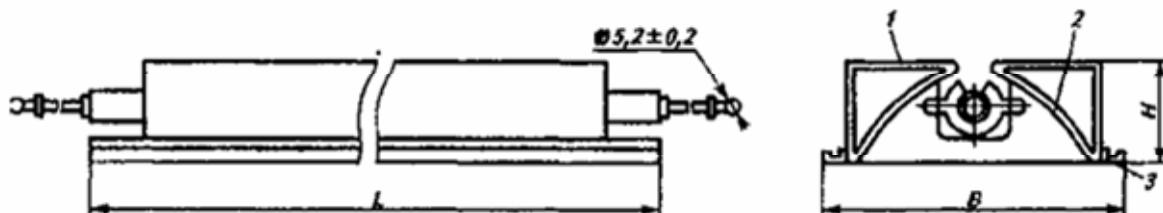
Общий вид конструкции и габаритные размеры светильника облучателя типа ББП01-30-001 У3,5
